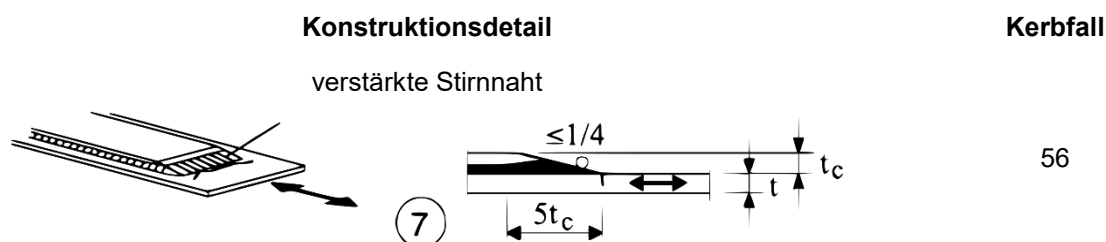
Gurtlamelle mit verstärkter Stirnnaht auf Walz- und geschweißten Trägern mit Kerbfalleinstufung nach DIN EN 1993-1-9 [1]
